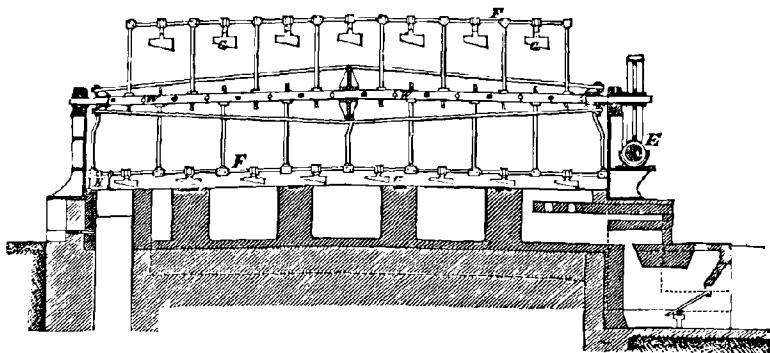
Chaudière de Thelen pour l'évaporation des lessives de soude (coupe longitudinale).
